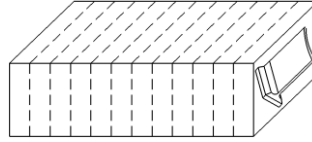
Схема вирізання заготовок лопаток з напівфабрикату після ІПД
